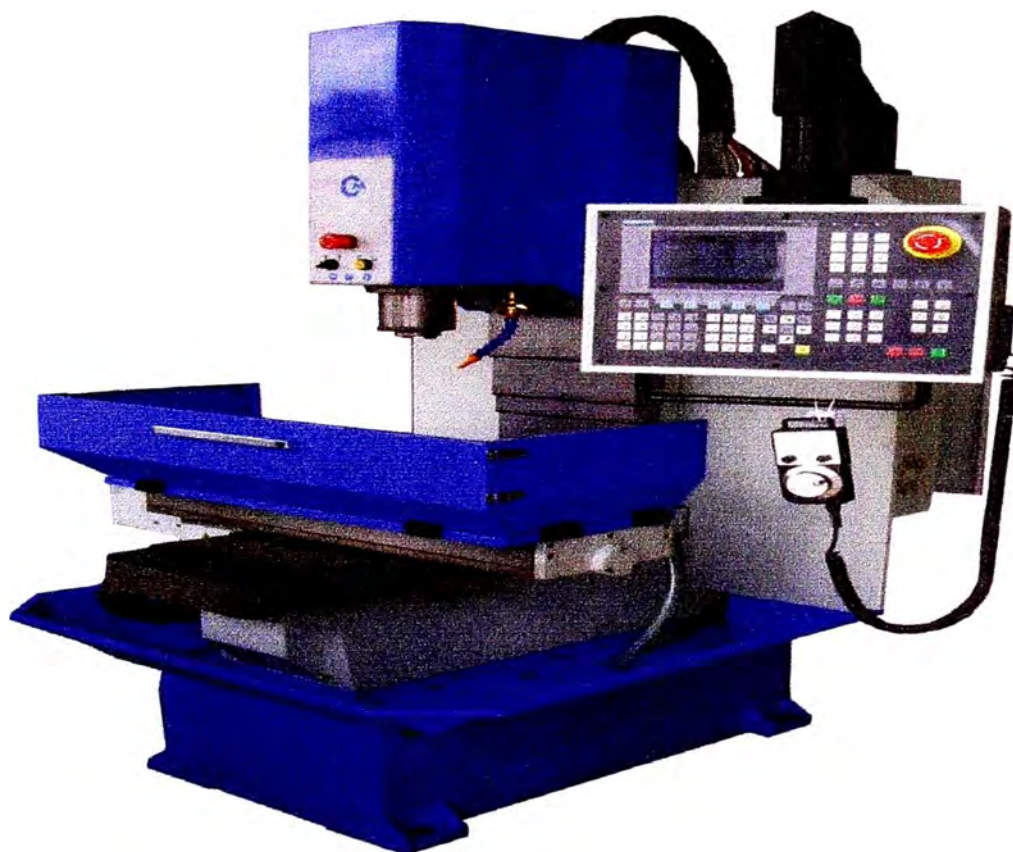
Fresadora CNC SM 280 (SIEMENS)
